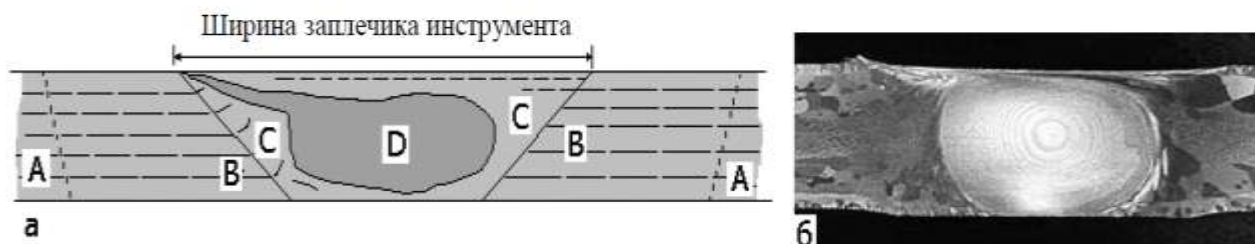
Схема строения поперечного сечения сварного соединения:
